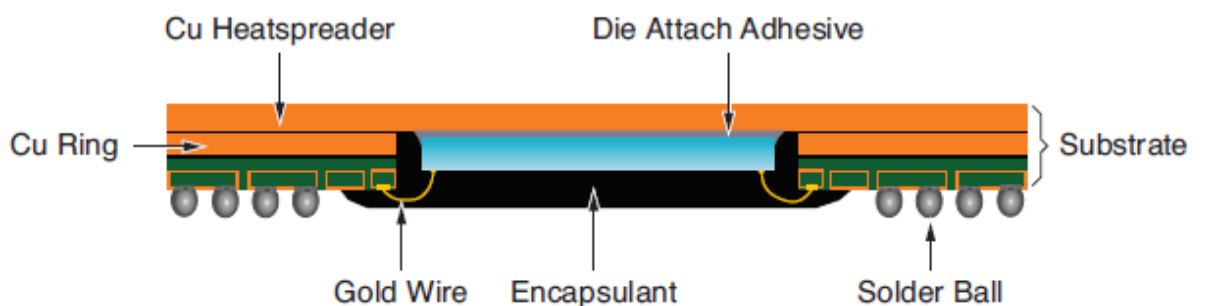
Befestigung des Chips von unten im Gehäuse /XIL 12/
